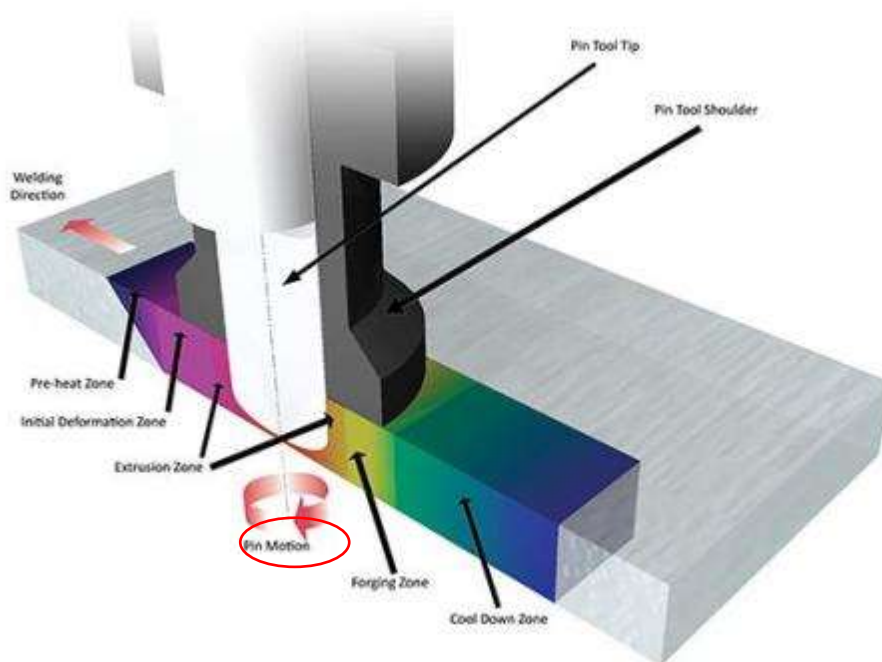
Áreas de la soldadura de fricción rotativa
